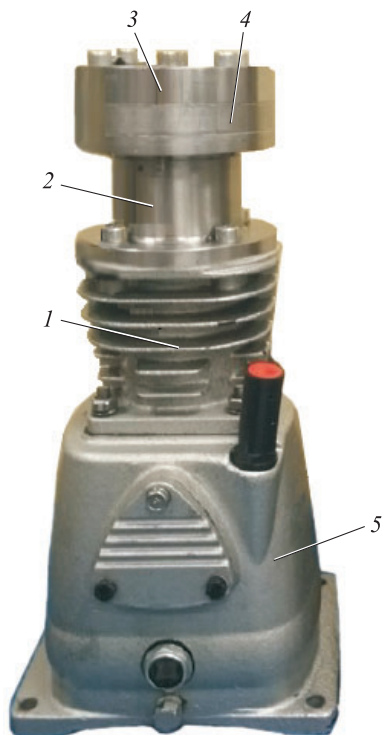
Внешний вид бескрейцкопфной ПГЭМОД с указанием основных деталей и узлов:
